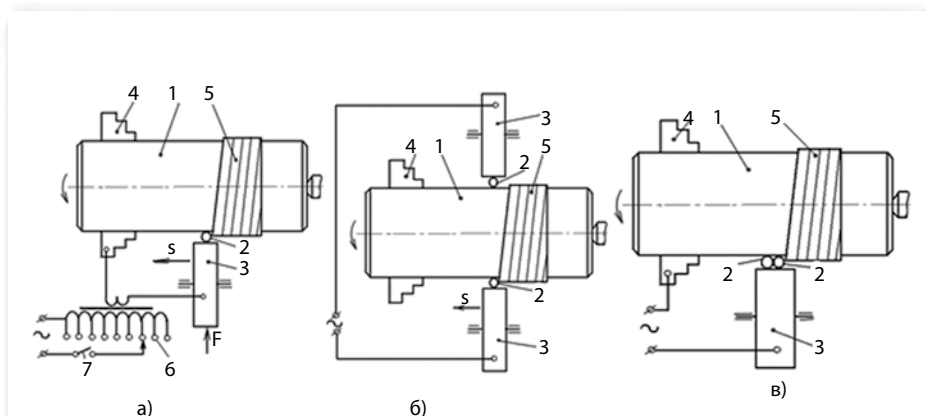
Схемы ЭКПП: а — основная; б — двухроликковая с двумя проволоками; в — однороликковая двумя проволоками. 1 — деталь; 2 — присадочная проволока; 3 — ролик-электрод; 4 — патрон; 5 — металлопокрытие; 6 — сварочный трансформатор; 7 — прерыватель тока
